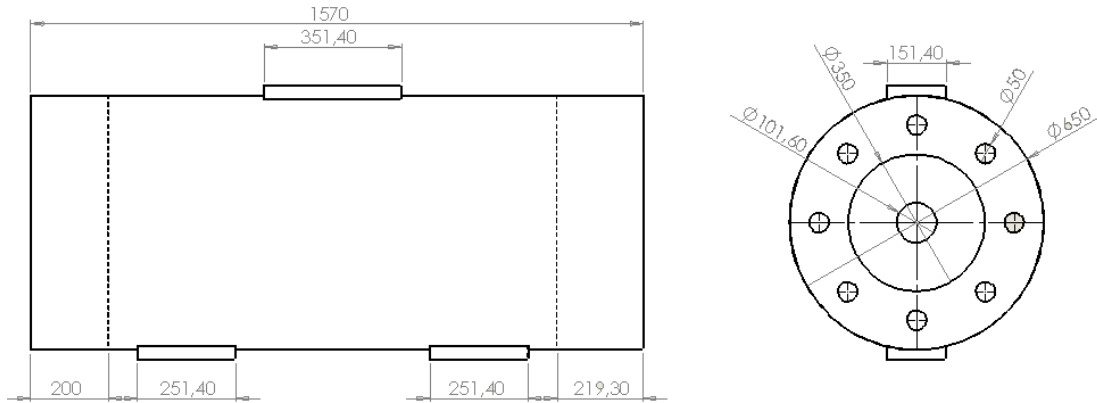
Croquis de la carcasa del intercambiador de calor.
